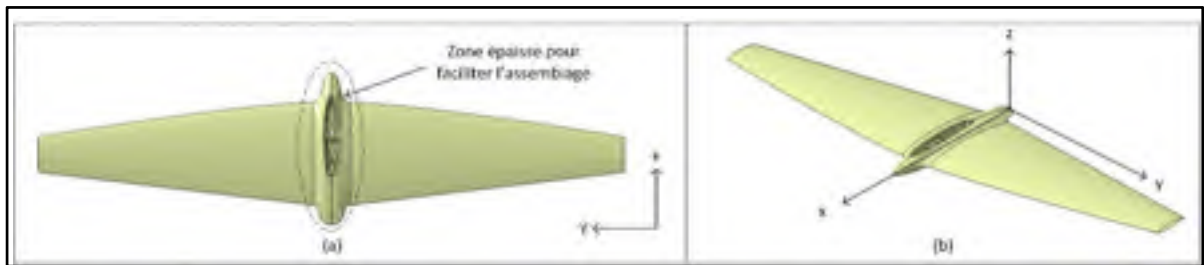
Aile du safran porteur; (a) Vue de dessus; (b) Vue isométrique
